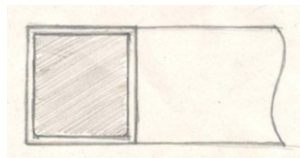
El perfil cuadrado se puede utilizar en el bastidor.
